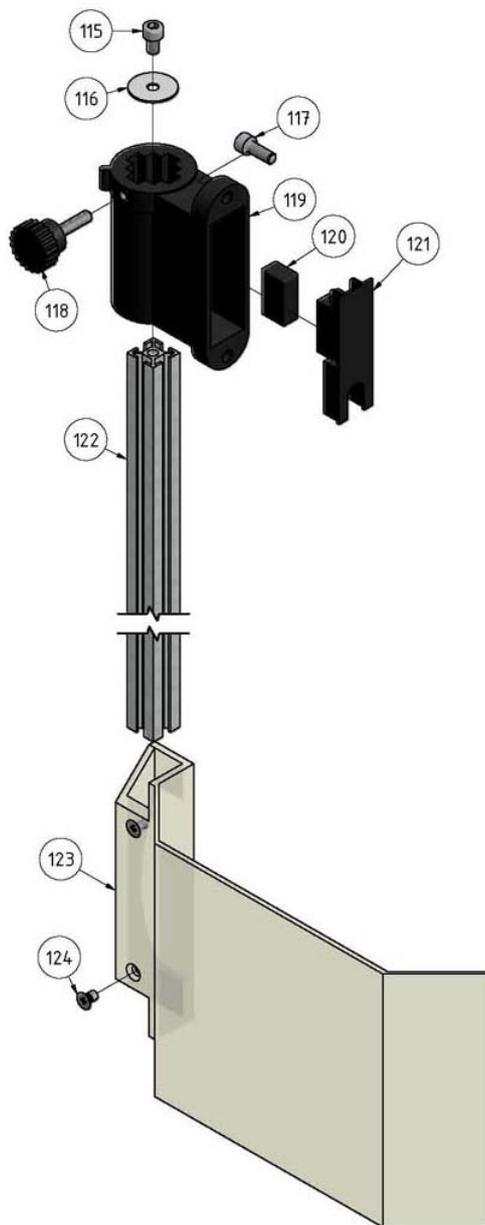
Fräskopf 6 von 6 - Milling head 6 von 6
